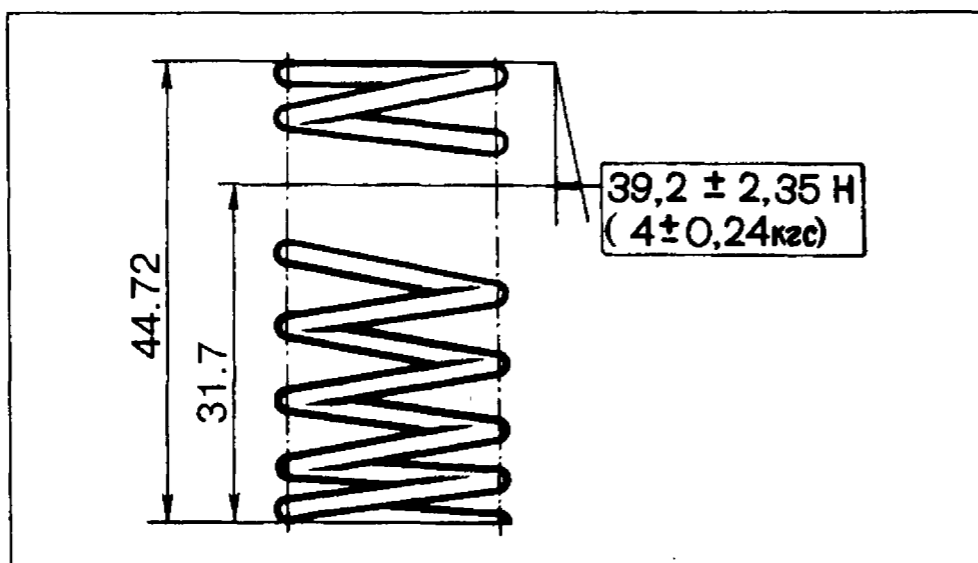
Основные данные для проверки пружины редукционного клапана масляного насоса
